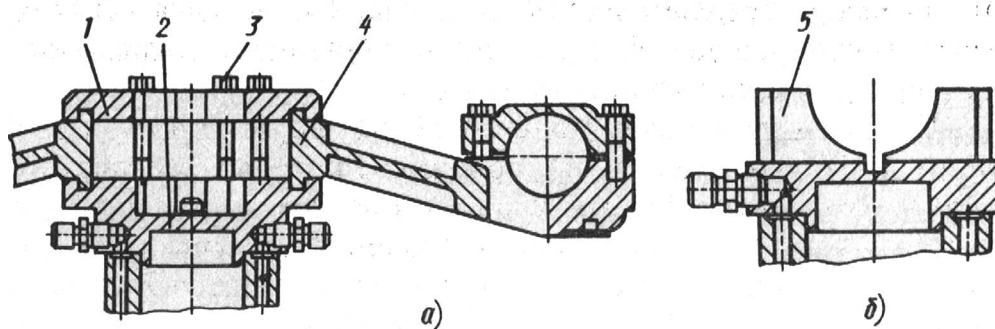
Устройства для крепления механизмов выдвижения-втягивания захватов: а — для крепления двух механизмов; б — для крепления одного механизма
